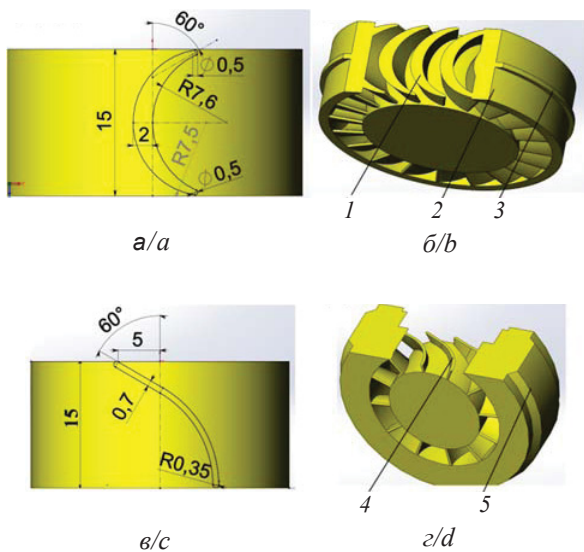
Форма лопаток ротора и соплового аппарата: а – размеры лопатки ротора; б – ротор в разрезе: 1 – лопатки, 2 – обод ротора, 3 – выступ лабиринтного уплотнения; в – размеры лопатки соплового аппарата; г – сопловой аппарат в разрезе: 4 – лопатки статора, 5 – корпус турбины
